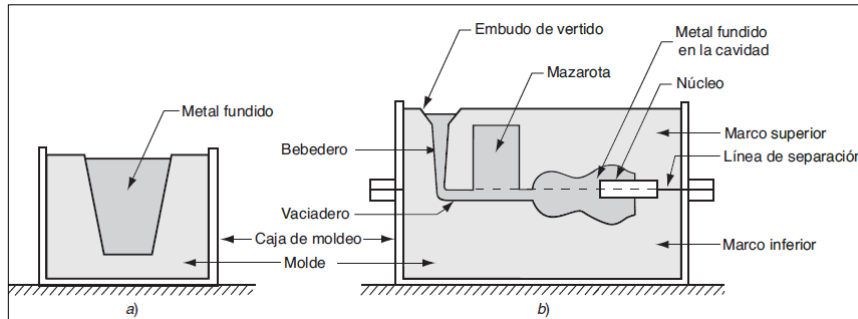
Formas de molde: a) molde abierto, b) molde cerrado
